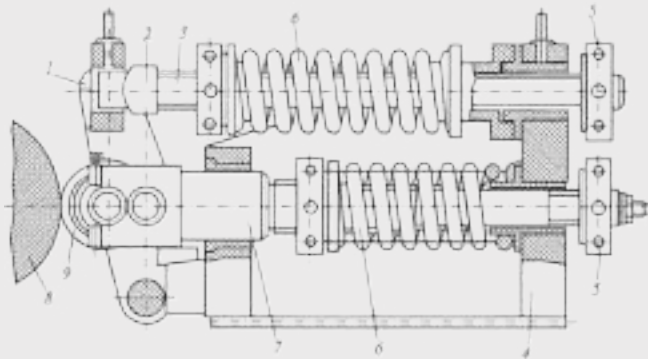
Двопружинний однороликовий обкатник: 1 — шток; 2 — головка верхнього штока; 3 — верхній шток; 4 — корпус; 5 — гайка; 6 — пружина; 7 — нижній шток; 8 — деталь; 9 — обкатний ролик
